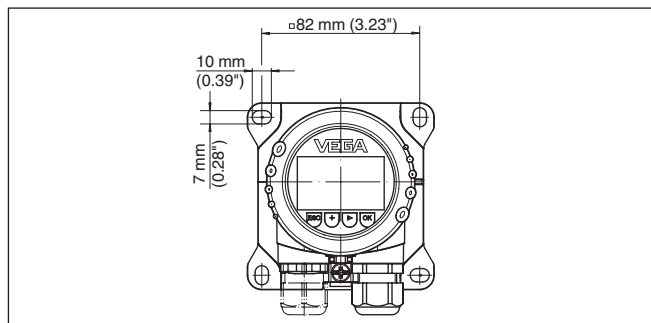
Dimensioni dei fori nel VEGADIS 81 per il montaggio a parete
